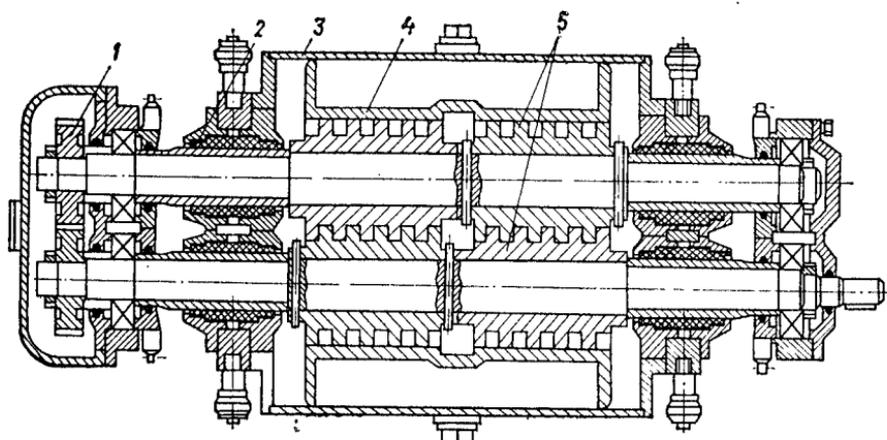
Двухвинтовой насос типа 2ВВ:
